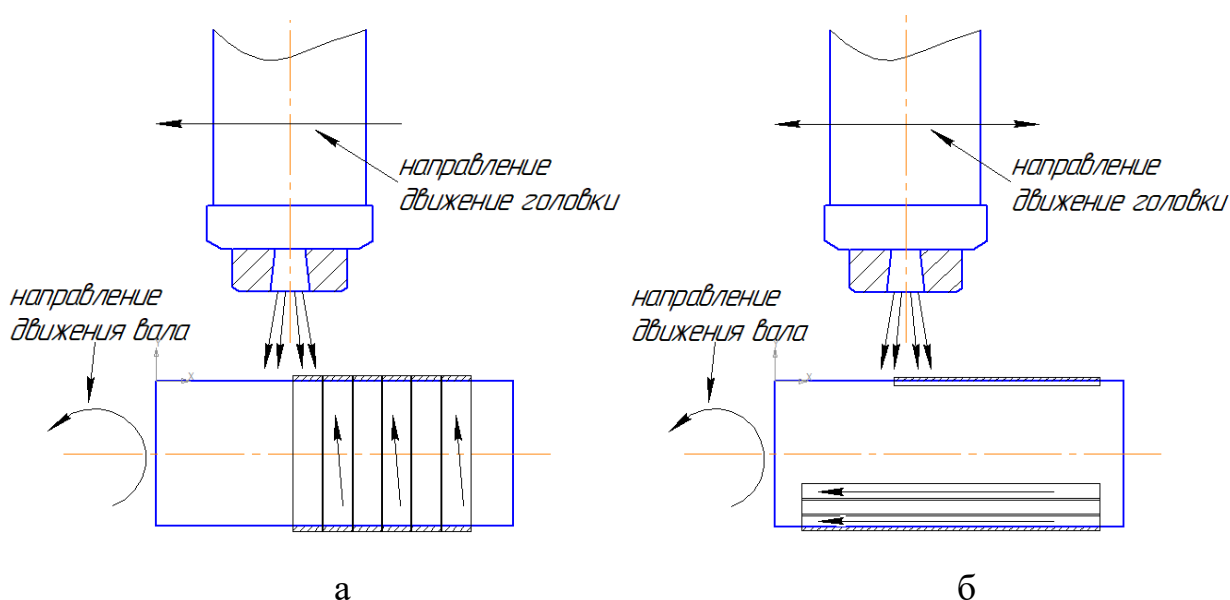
Схемы движения детали относительно напыляемой ГОЛОВКИ
